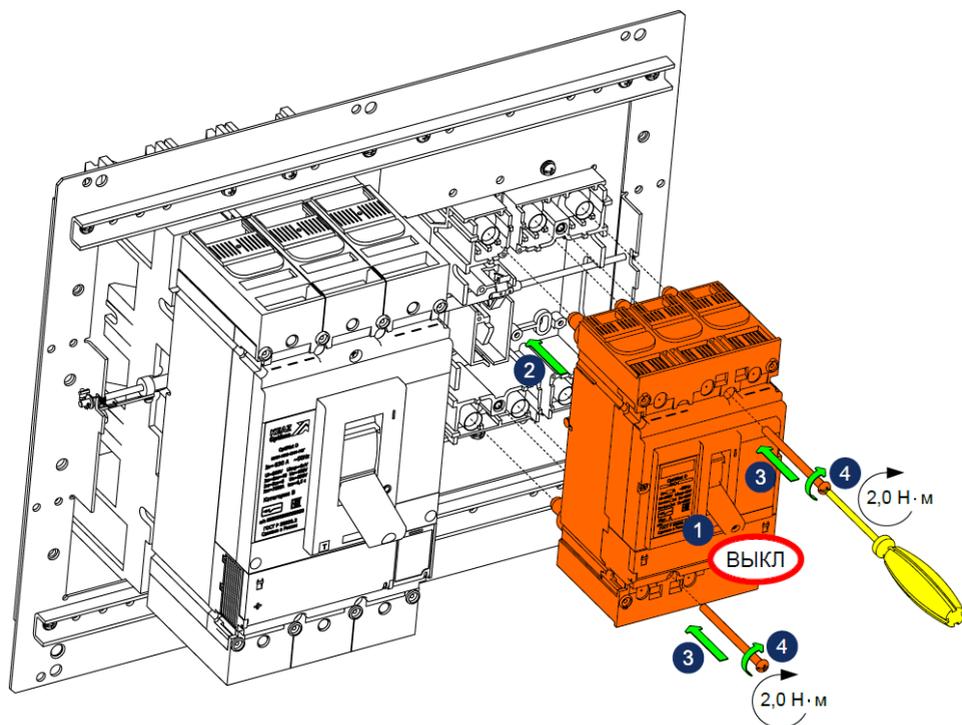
Установка механизма блокировки на стационарный выключатель OptiMat D100, D160 и D250
